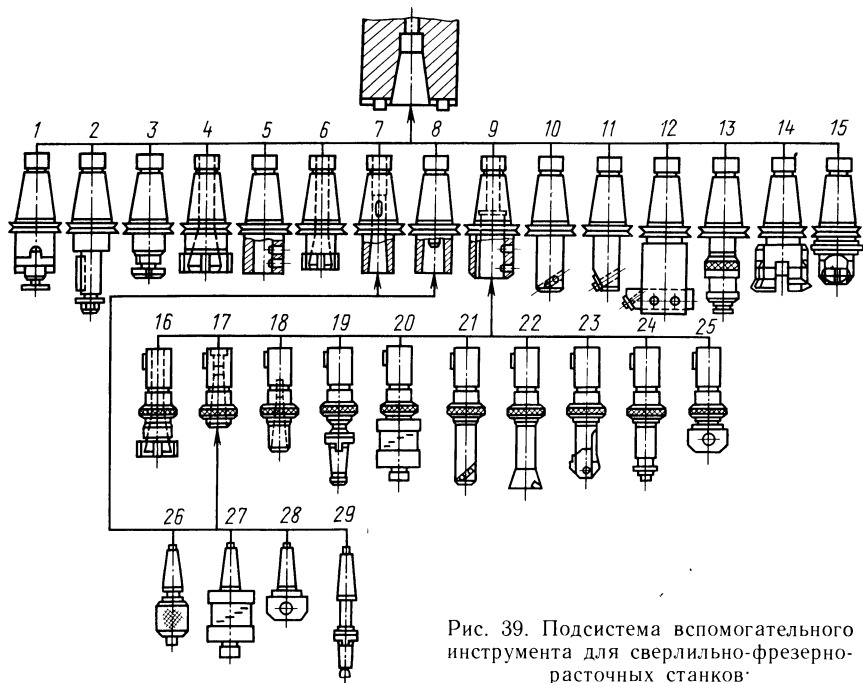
Подсистема вспомогательного инструмента для сверлильно-фрезерно-расточных станков
